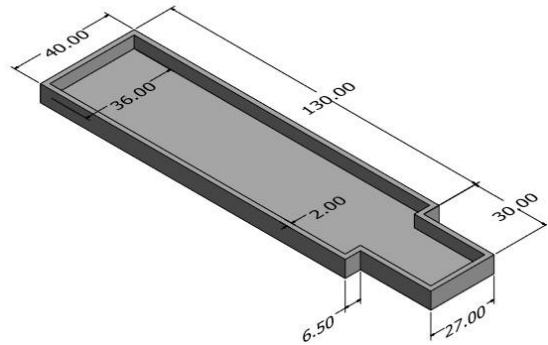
Dimensiones del molde inferior. Vista isométrica. Medidas dadas en milímetros (mm)
